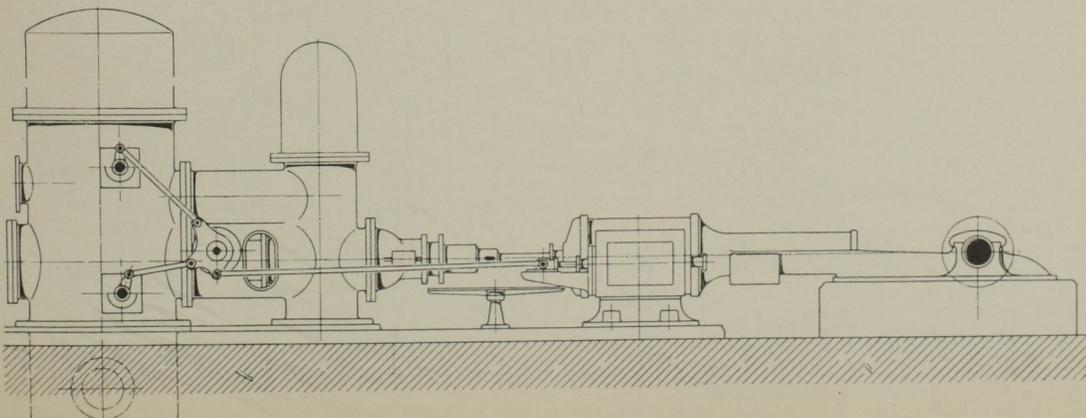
Wasserwerksmaschine der Stadt Kladno.
